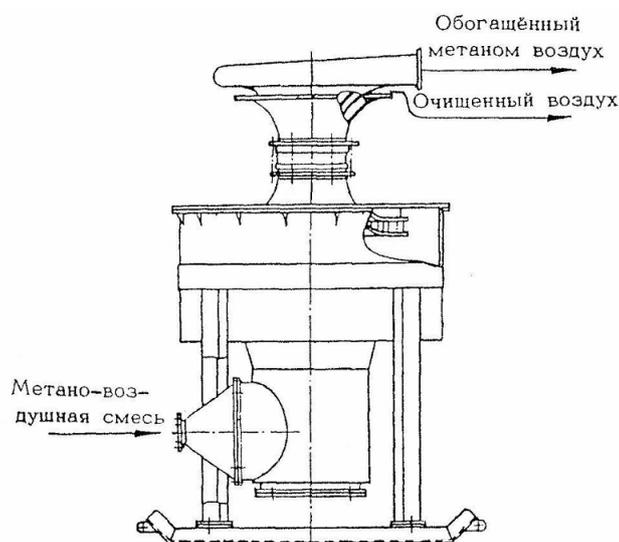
Общий вид газоразделительного сепаратора: 1 — корпус сепаратора; 2 — пластина; 3 — вертикальный коллектор для метана; 4 — канал для поступления исходной смеси; 5 — клапан; 6 — внутренняя часть сепаратора; 7 — мембрана; 8 — канал для МВС; 9 — переборки; 10 — мембранный слой; 11—13 — выход очищенного воздуха; 14—16 — выход обогащенного метана
